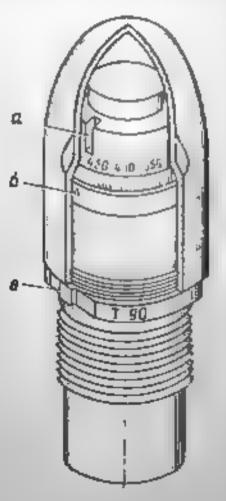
Трубка Т 90- и — услащвочный паз. б установоч ная риска в - ус тановочный выступ
